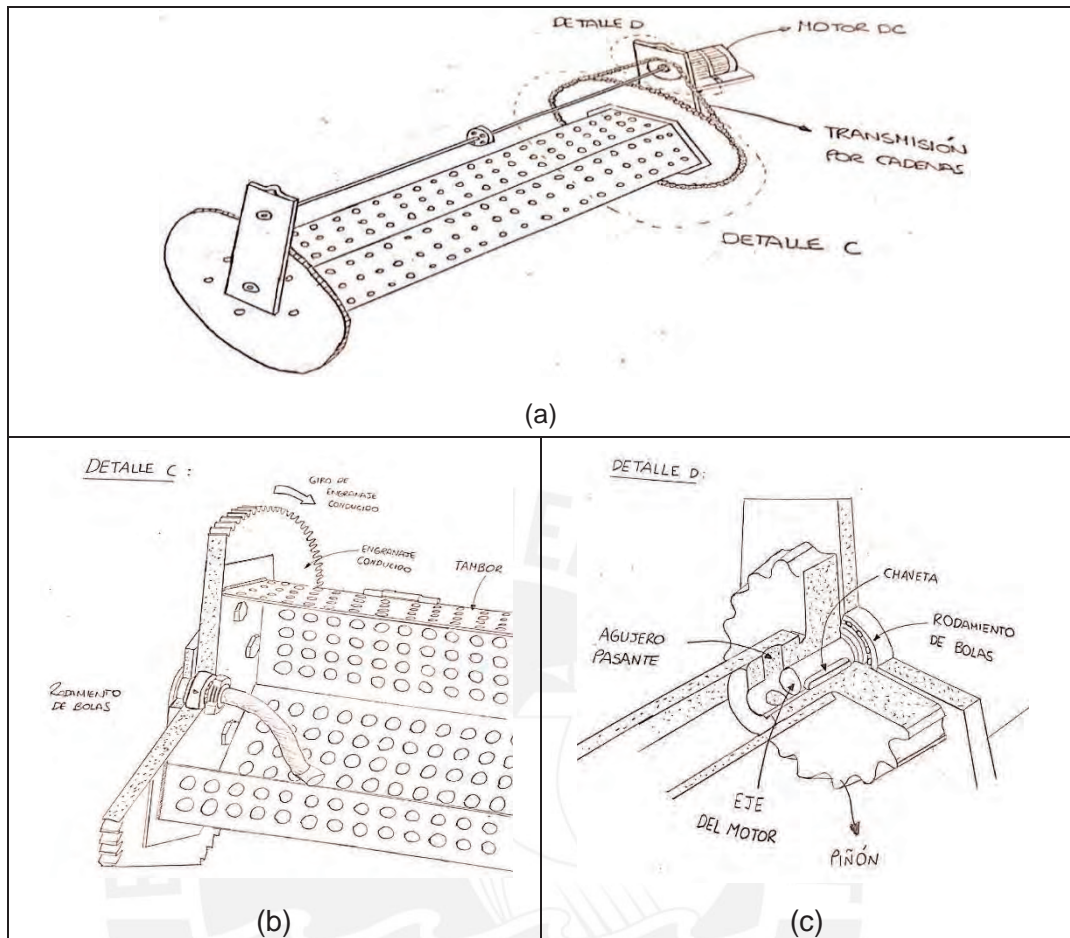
Bosquejo del ensamble del tambor. a) Vista isométrica del ensamble. b) Primer detalle del ensamble. c) Segundo detalle del ensamble. Fuente: Propia
